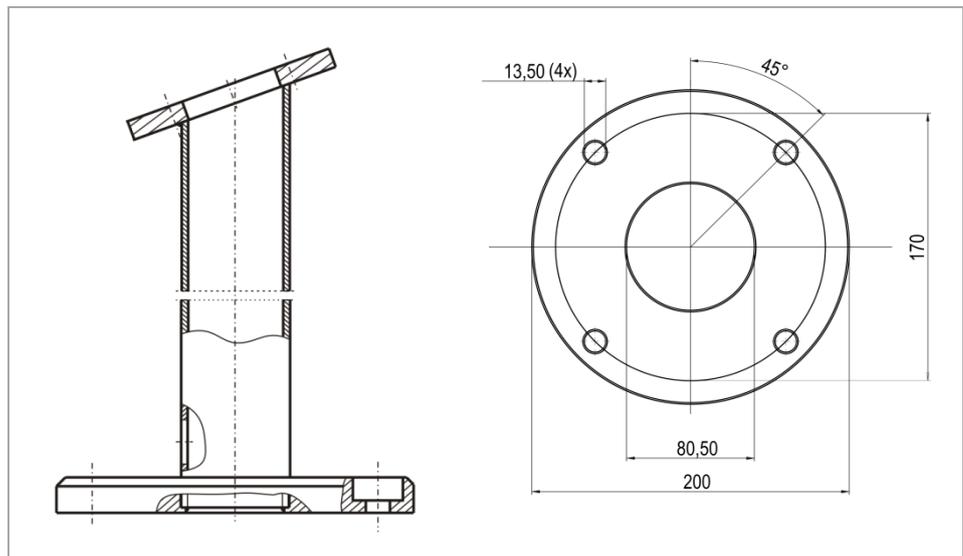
Standfuß - Bohrbild Bodenplatte
